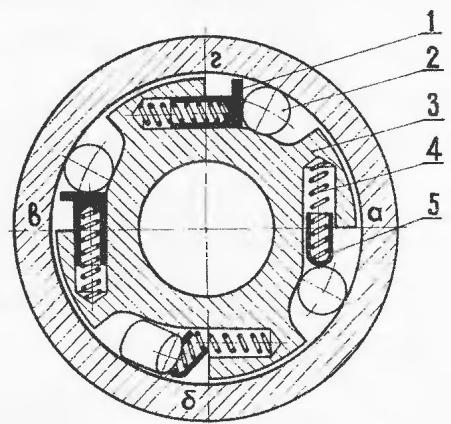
Так ремонтируется муфта свободного хода: 1 — новый плунжер; 2 — ролик; 3 — ведущий корпус муфты; 4 — пружина; 5 — старый плунжер; а — заводская конструкция; б — типичная неисправность; в и г — ремонт при помощи заклепок.
